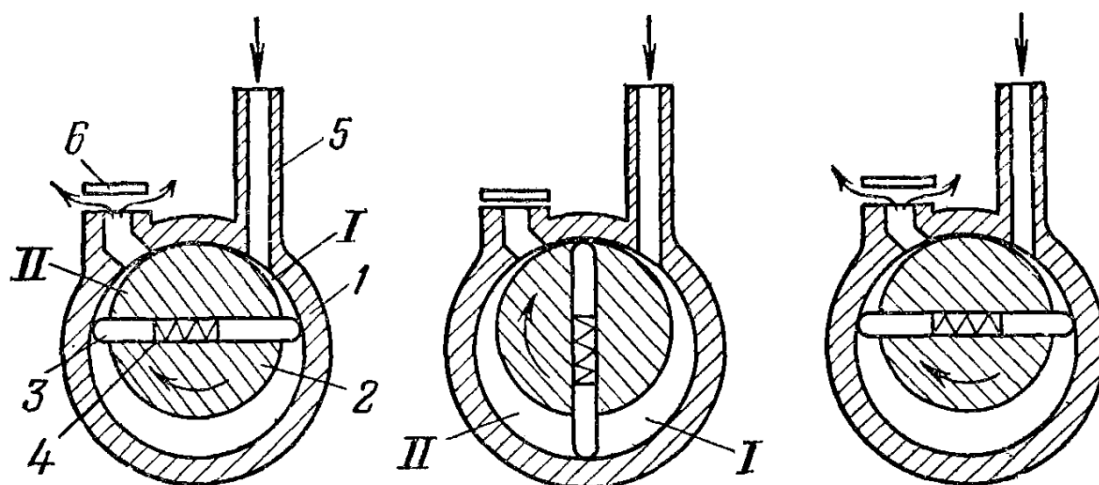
Принцип действия пластинчато-роторного насоса. 1 – цилиндрический корпус; 2 – эксцентричный ротор; 3 – пластины; 4 – пружина; 5 – впускной патрубок; 6 – клапан; I – полость всасывания; II – полость сжатия [5, с. 94]
